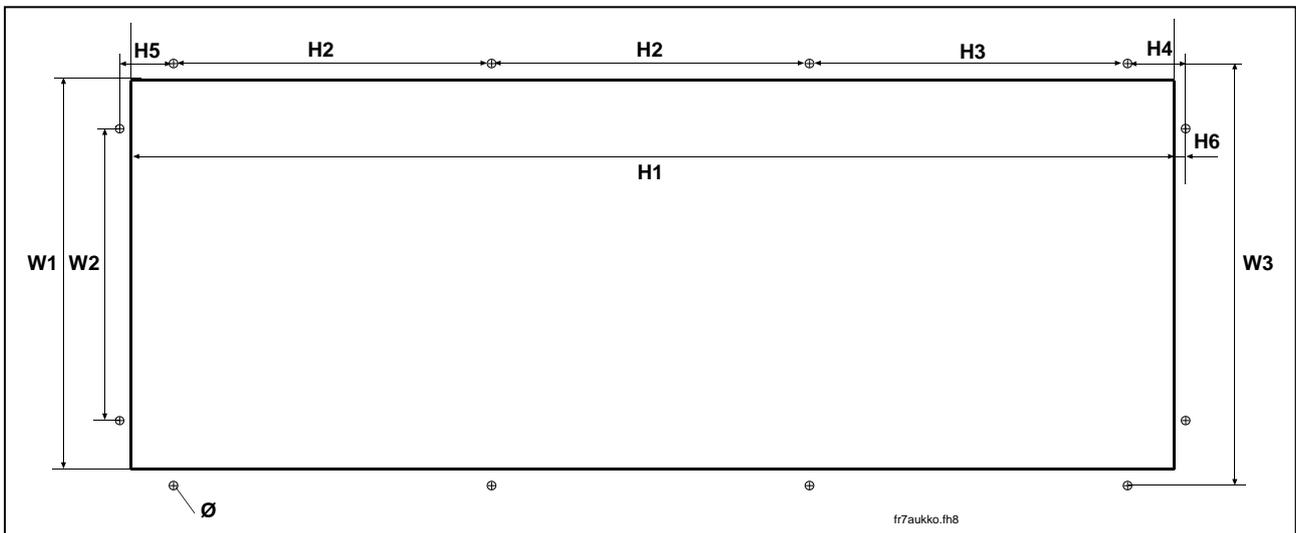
5. Ouverture pour le montage traversant sur bride, tailles FR7 et FR8
